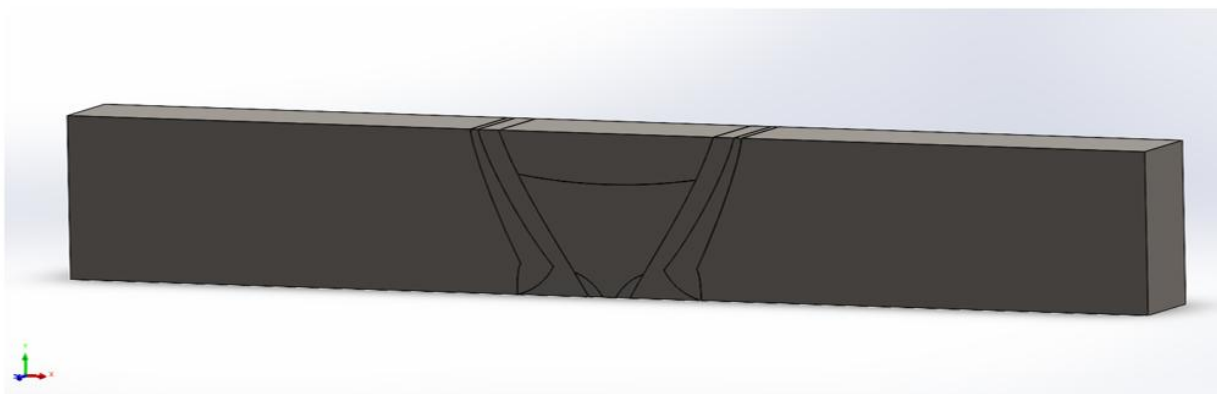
Численная модель образца с механически неоднородным сварным соединением
